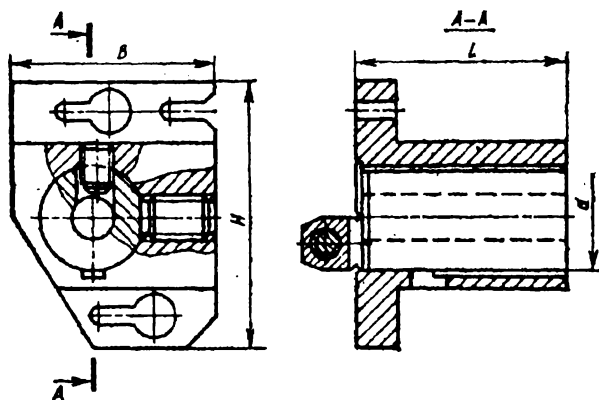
Инструментальный блок для установки расточных резцов и стержневых инструментов в револьверную головку
